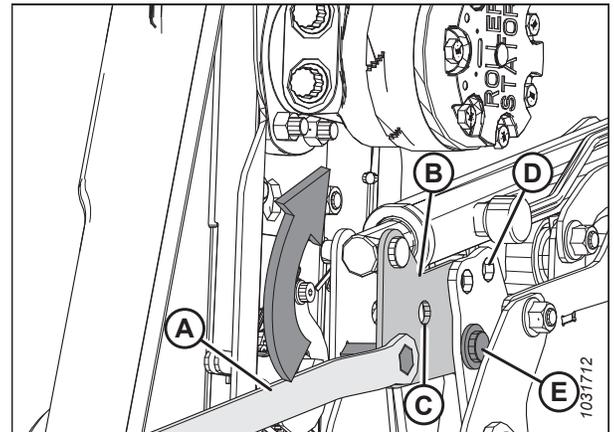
Cilindro del braccio centrale sinistro – Posizione avanzata
